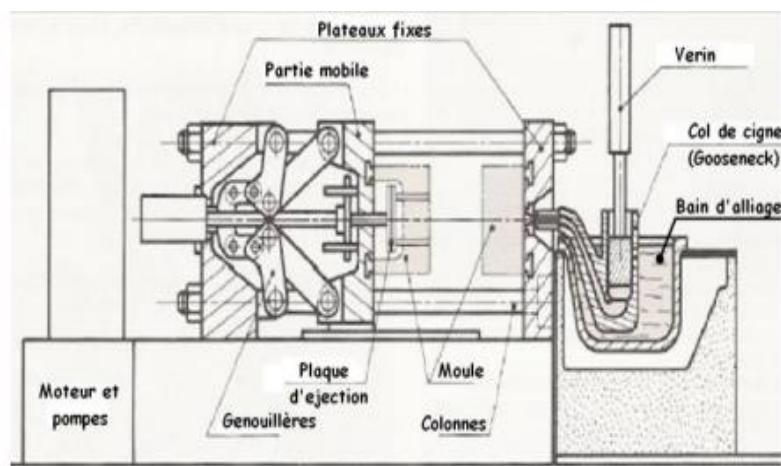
Principe du moulage en coquille sous pression de machines à chambre chaude.
